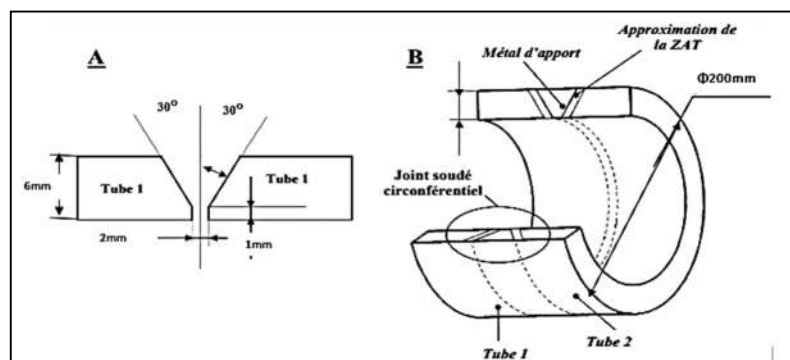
Géométrie de la section du joint soudé du pipeline
